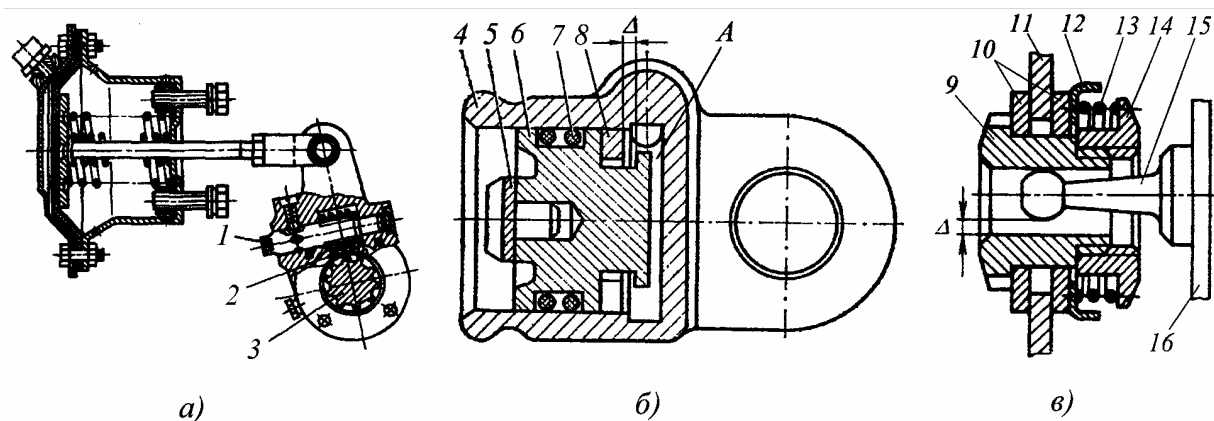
Устройства регулировки зазора между фрикционной накладкой и тормозным барабаном:
